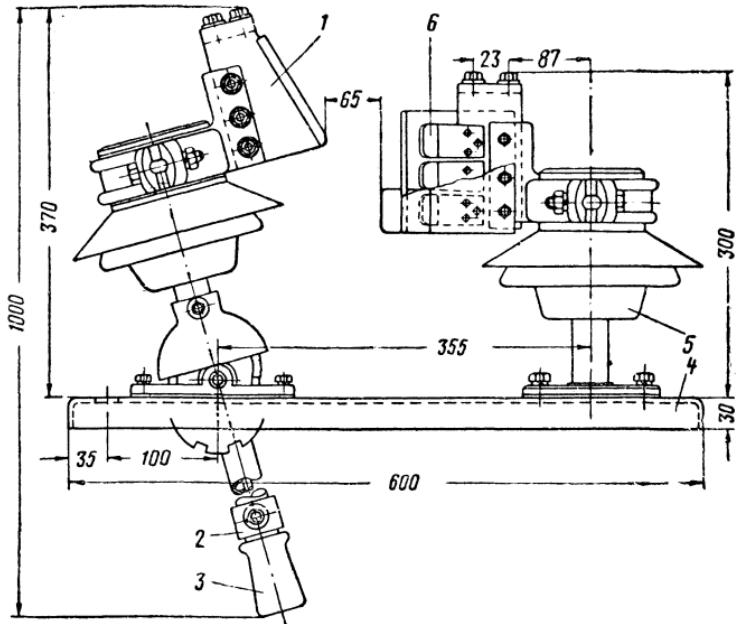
Разъединитель высоковольтный наружной установки РВН-1:
